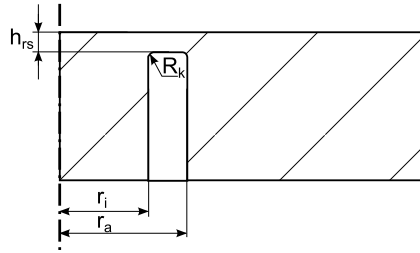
Geometrieparameter der Flächenlastspiegel mit rückseitiger Ringnut.
